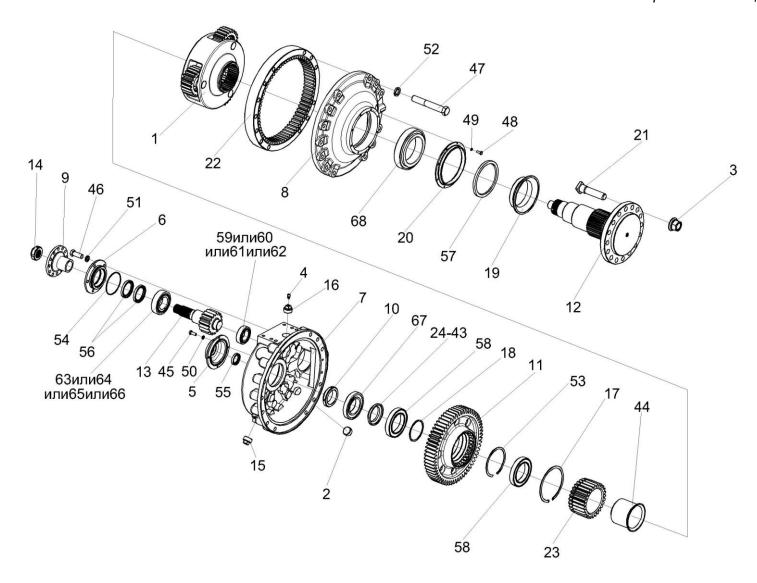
Редуктор бортовой КВК 0106020 (изображено) Рисунок 103 — Редуктор бортовой КВК 0106020-01 (зеркальное отражение)
